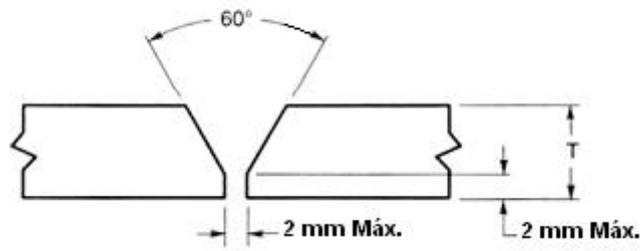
Junta a Tope Tubular, Sin Respaldo– Calificación de Soldador
